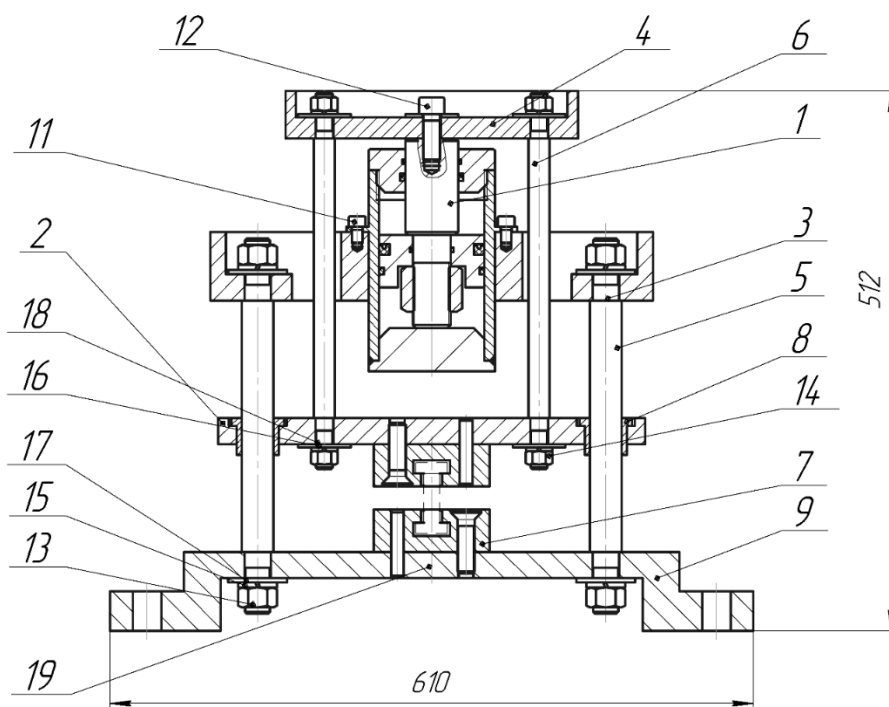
Приспособление для растяжения цилиндрических образцов с буртиками
